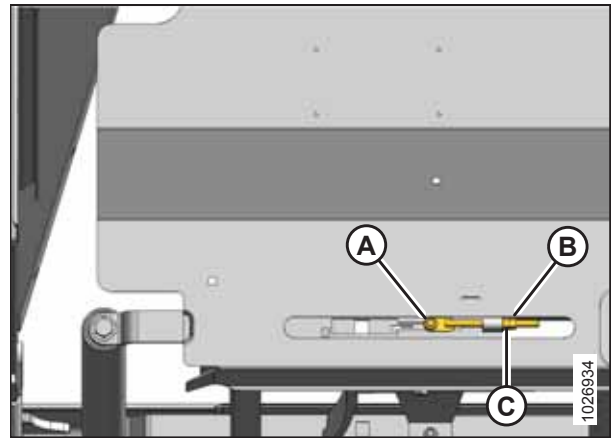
Rodillo tensor de la plataforma izquierda: lado derecho opuesto
